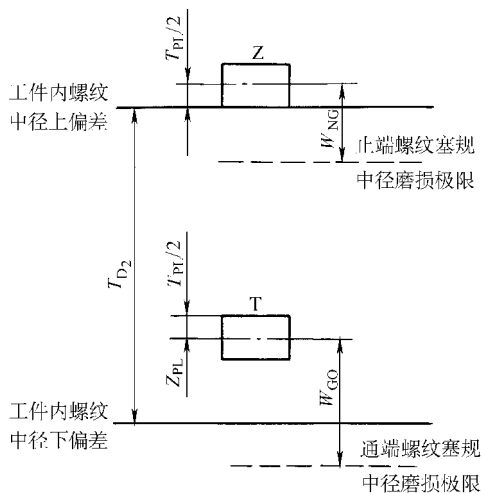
螺纹塞规的螺纹中径公差带
